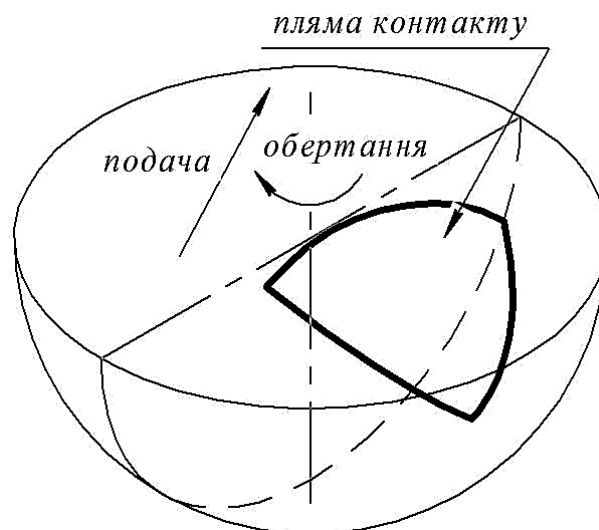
Пляма контакту під час висхідного зустрічного фрезерування сферичною кінцевою фрезою
